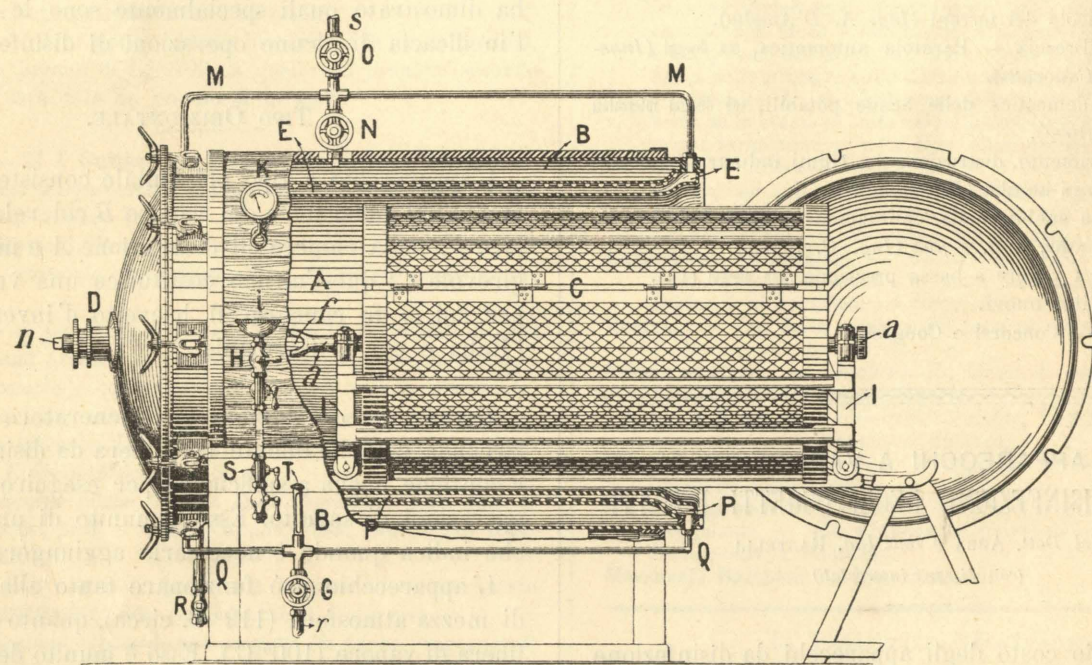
Vista e sezione longitudinale dell'apparecchio di disinfezione ABBA-RASTELLI (tipo orizzontale).
